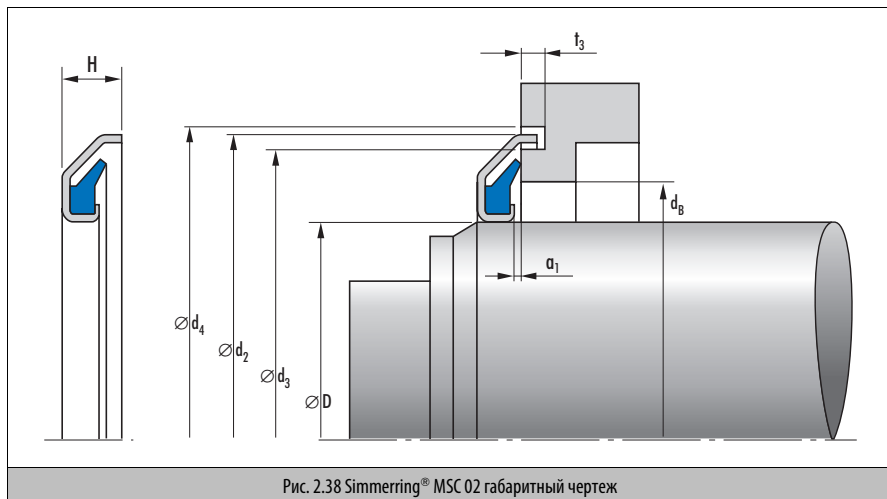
Simmerring® MSC 02 габаритный чертёж
